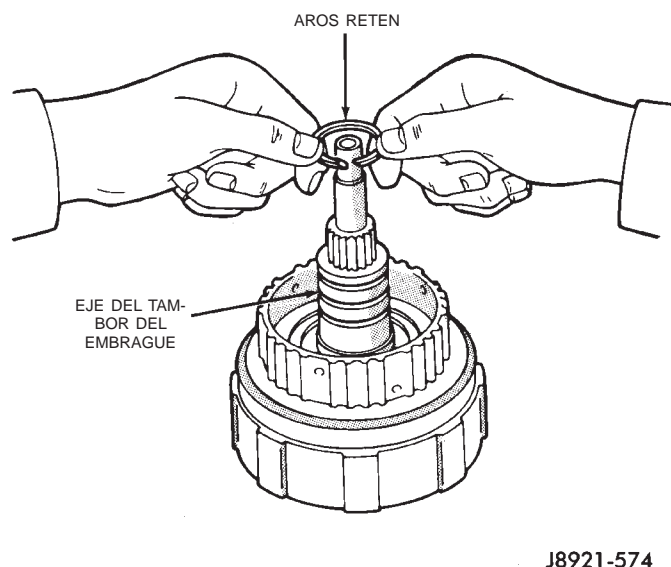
Desmontaje de los aros retén del tambor del embrague
